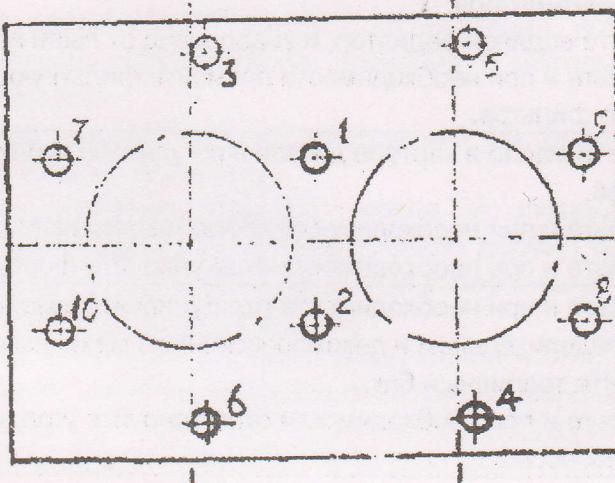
Последовательность затяжки гаек крепления головки цилиндра
